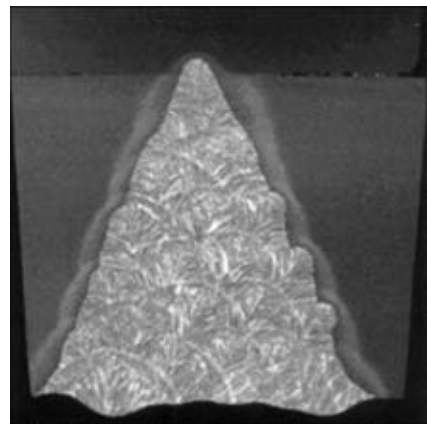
Микрошлиф сварного соединения стали толщиной 25,4 мм, выполненного в потолочном положении способом сварки сдвоенным электродом
